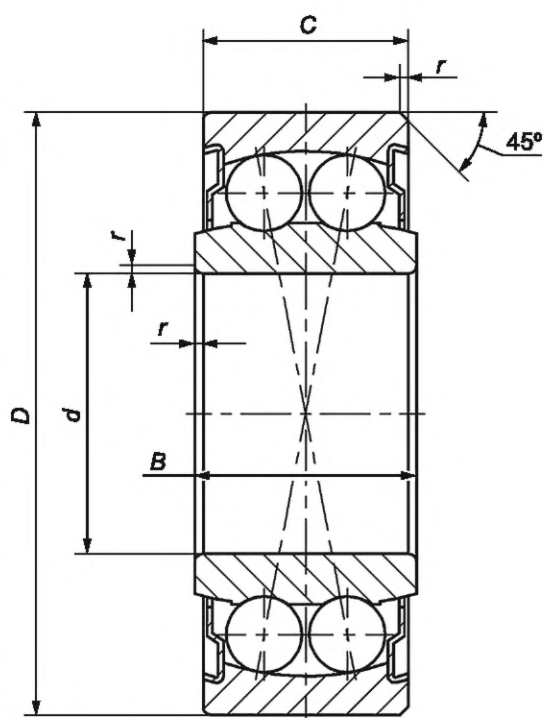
Конструктивное исполнение 97, шариковый радиальный сферический двухрядный
